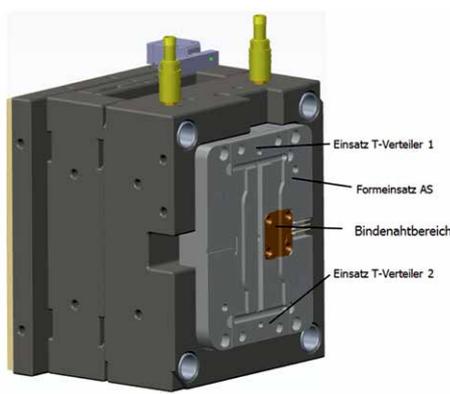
Auswerferseitige (AS) Werkzeughälfte des In-Mould-Aktuatorik Werkzeuges
